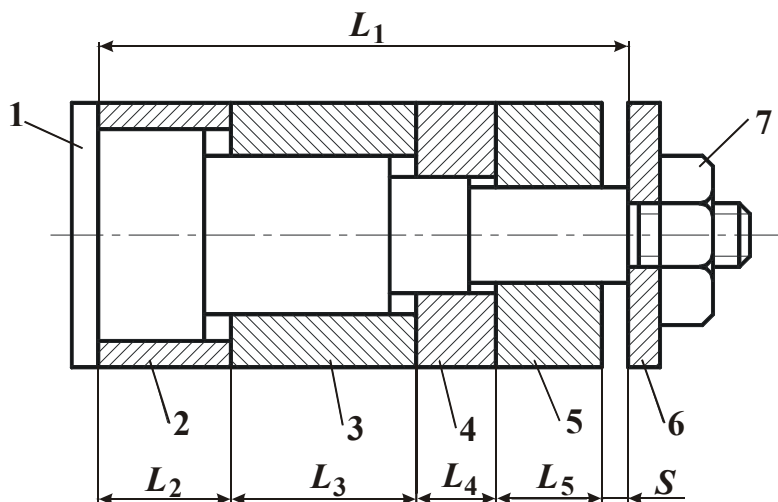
Модель механизма (сборочного узла): 1 - ступенчатый вал; 2...5 - втулки, 6 - шайба; 7 – гайка.
